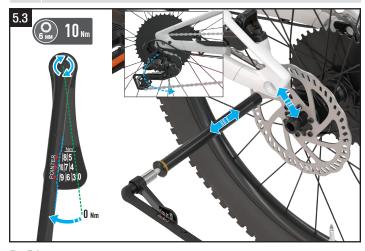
DÉMONTAGE DE LA ROUE ARRIÈRE
